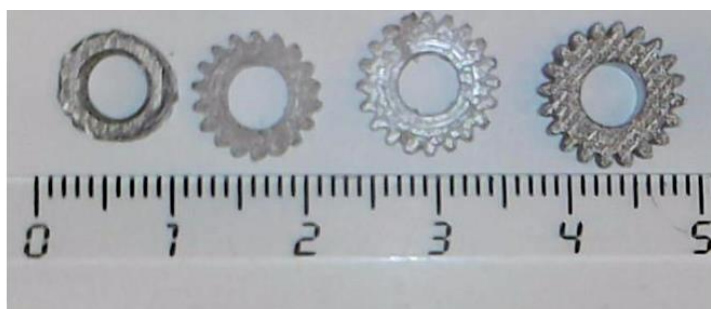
Фотографии дефектной шестерни, полимерных прототипов и шестерни из титана для стойки ротационного вискозиметра
